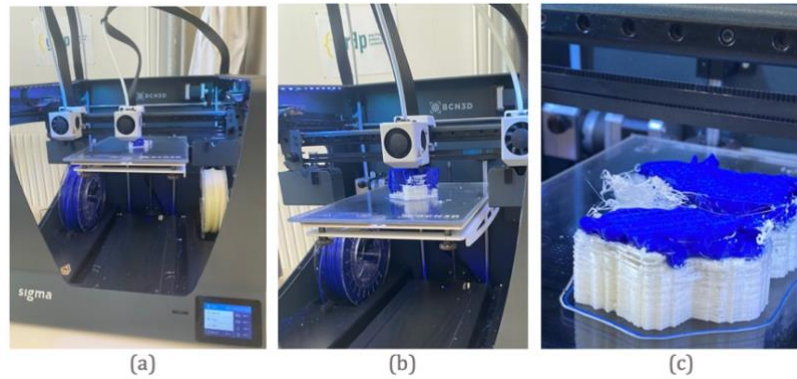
(a) procés d'impressió. (b) i (c) problema en la impressió del material de suport.
